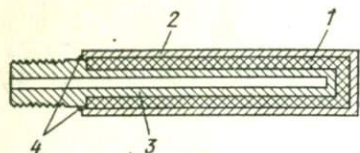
Многослойный реактор: 1 — молибденовый силовой корпус, 2 — защитный кожух из нержавеющей стали, 3 — вкладыш из никеля, 4 — сварные герметичные швы
